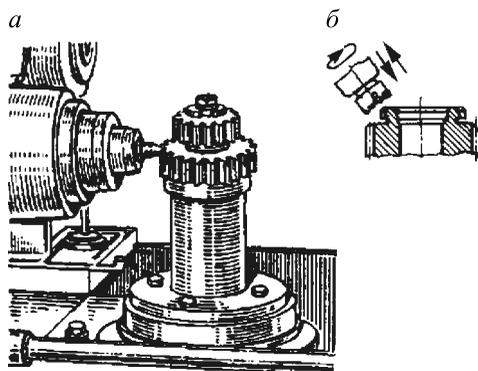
Закругление зубьев цилиндрических зубчатых колес
